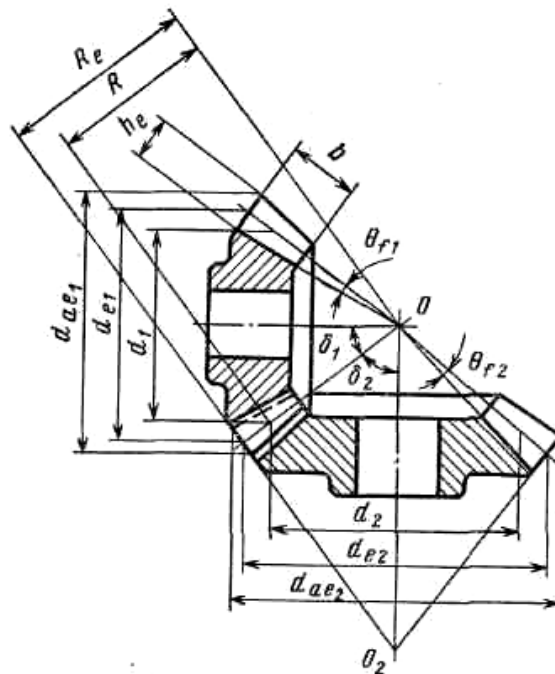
Схема передачи коническими зубчатыми колёсами
